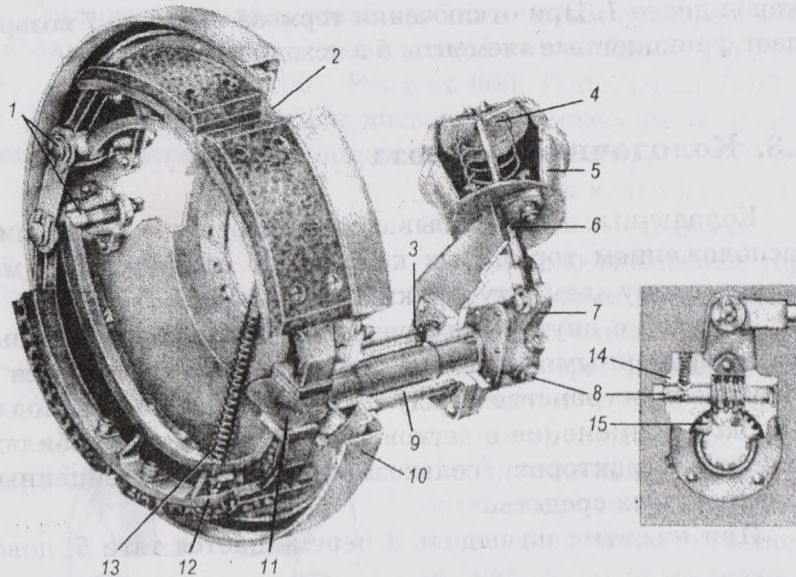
Колесный тормоз трактора Т-150К: 1 - эксцентрические оси; 2 - щит; 3 - масленка; 4 - диафрагма; 5 - корпус тормозной камеры; 6 - шток; 7 - регулировочный рычаг; 8 - червяк; 9 - кронштейн; 10 - кожух; 11 - кулак; 12 - тормозная колодка; 13 - пружина; 14 - шариковый фиксатор; 15 - червячная шестерня
